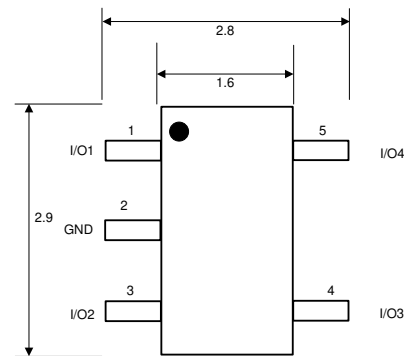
ESDS314 DBV Package, 5-Pin SOT23 (Top View)
